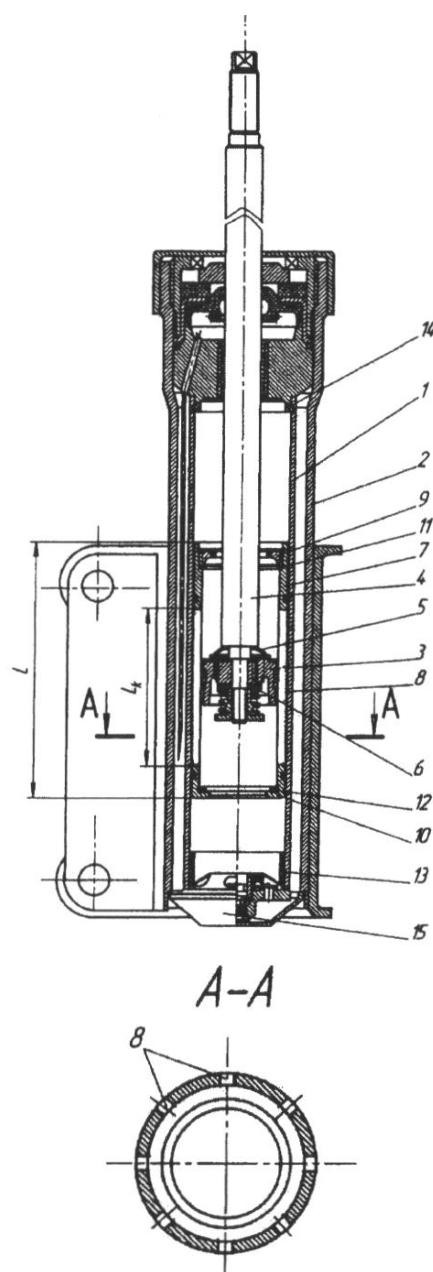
Амортизатор с плавающим цилиндром:
